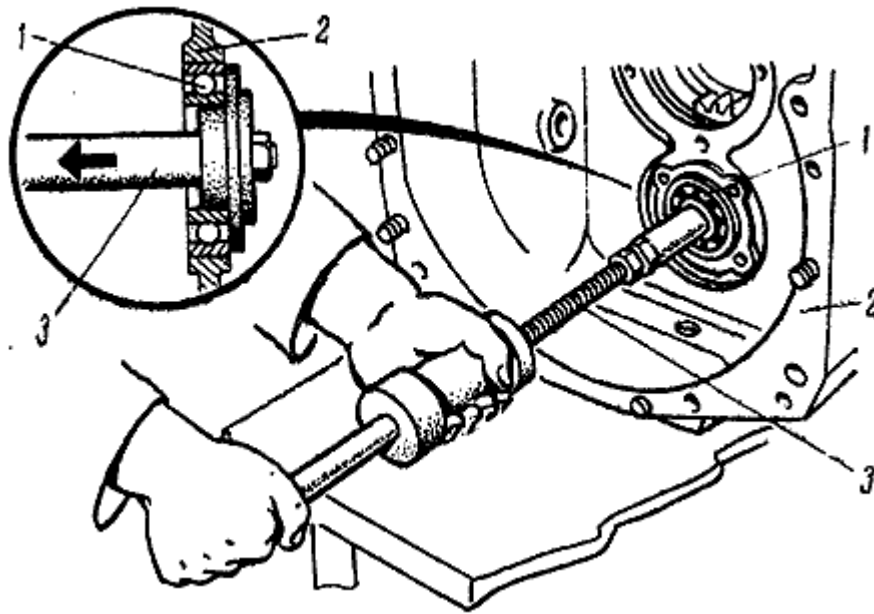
Выпрессовка подшипника из корпуса сцепления:
